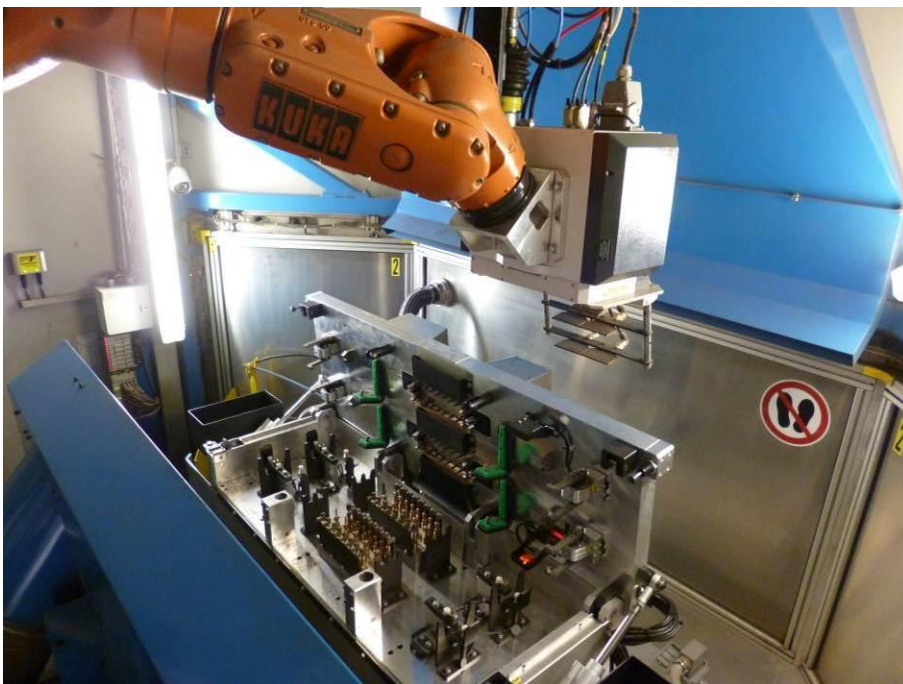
Innenansicht Laser-Remote-Schweißanlage B&S
